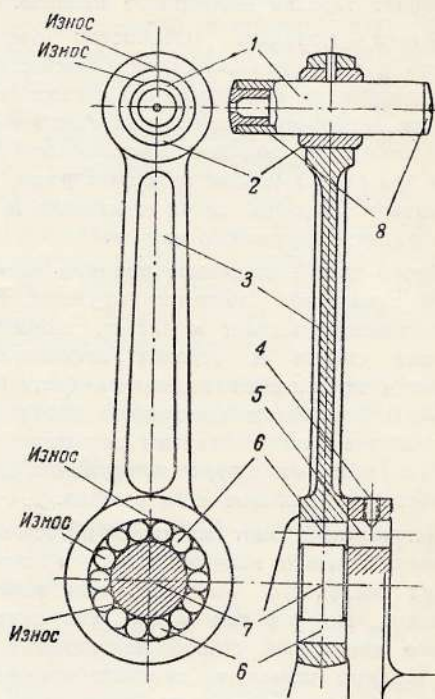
Шатун: 1—палец шатуна; 2—втулка верхней головки шатуна; 3—шатун; 4—стопорный винт; 5—пробка; 6—ролики нижней головки шатуна; 7—шейка коленчатого вала; 8—грибок
